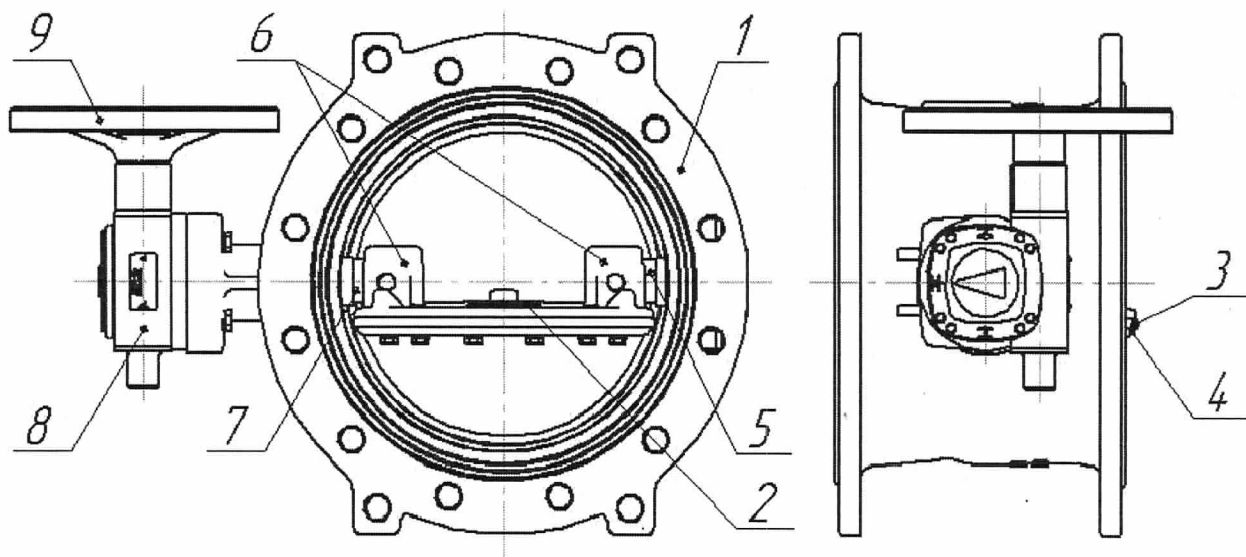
Устройство затвора с ручным приводом и штурвалом
